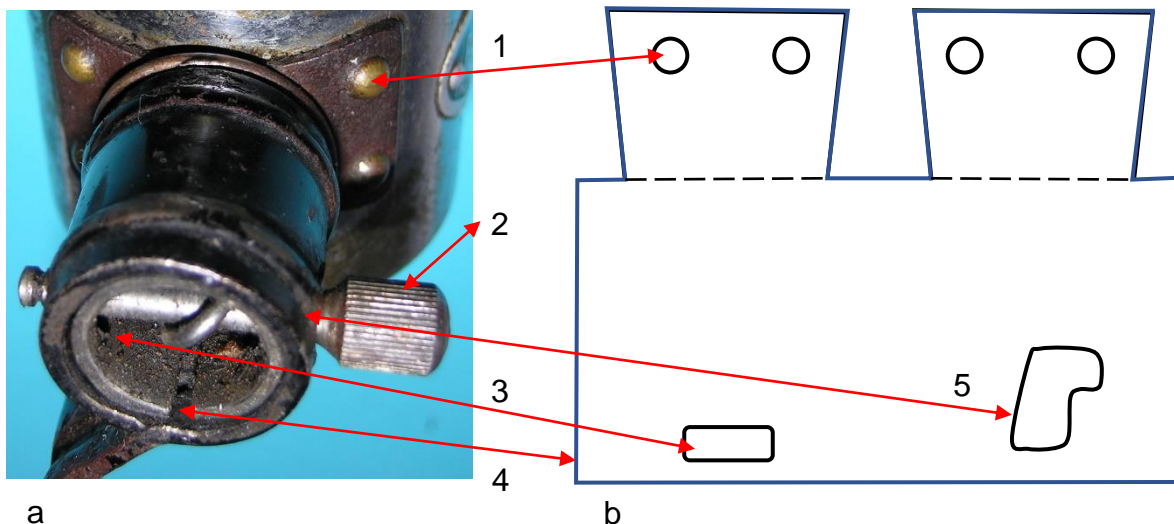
Ausführung des Drehbolzens als Rohr mit angeschnittenen Flanschhälften: a) Kippvorrichtung ohne Schutzkappe, b) Prinzipieller Blechschnitt zur Umformung zum Drehbolzen mit Flansch; 1- Nietlöcher, 2- Bedienungshebel und Sperrstift, 3- Langloch in Drehrichtung des Dynamokörpers, 4- Längsschlitz im Drehbolzen, 5- Axiales Langloch mit Rastnut
